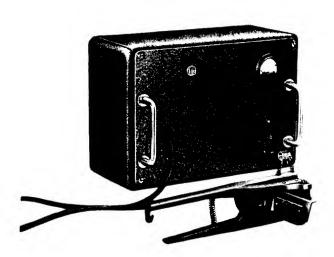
Hochirequenz-Schweissgerät Type ZDK-01-A.
